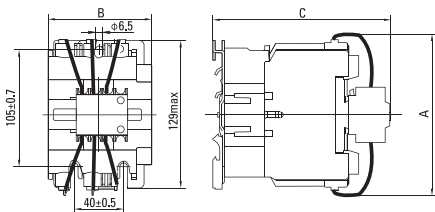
Габаритные и установочные размеры контакторов 63-95квар
